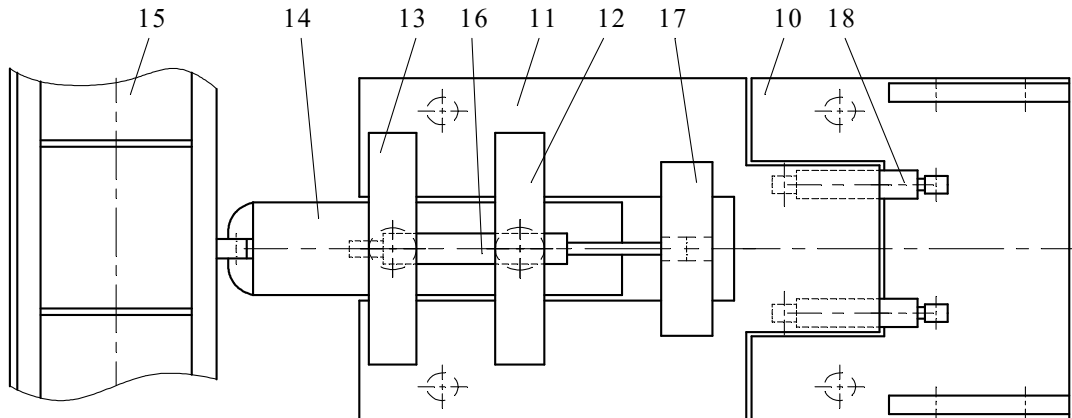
СМК с телескопическими перекрытием и основанием (вид сверху на основание)
